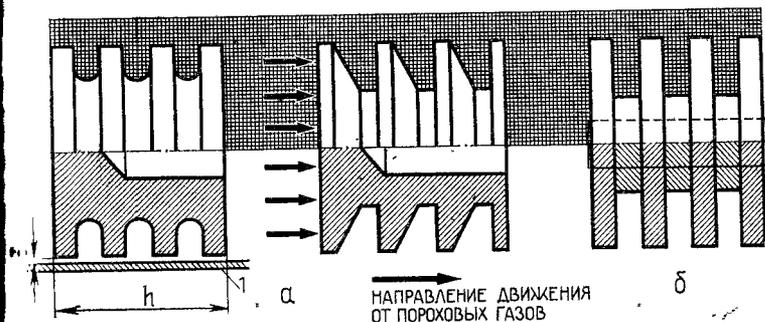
Формы гребешков лабиринтных уплотнений: а — точеный из дерева; б — сборный из картона; 1 — корпус модели
